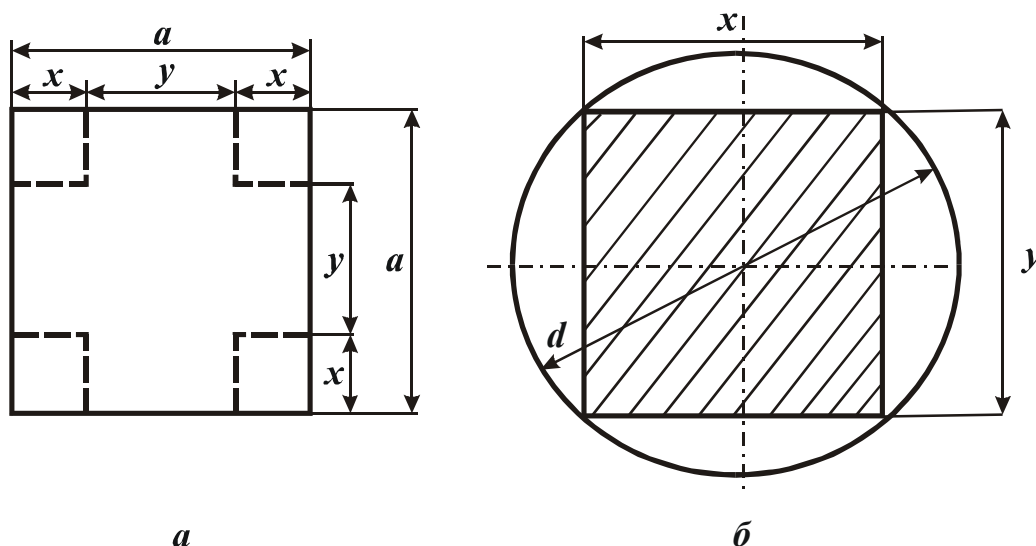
Расчетные схемы: а - развертка заготовки для изготовления; б- сечение балки.
